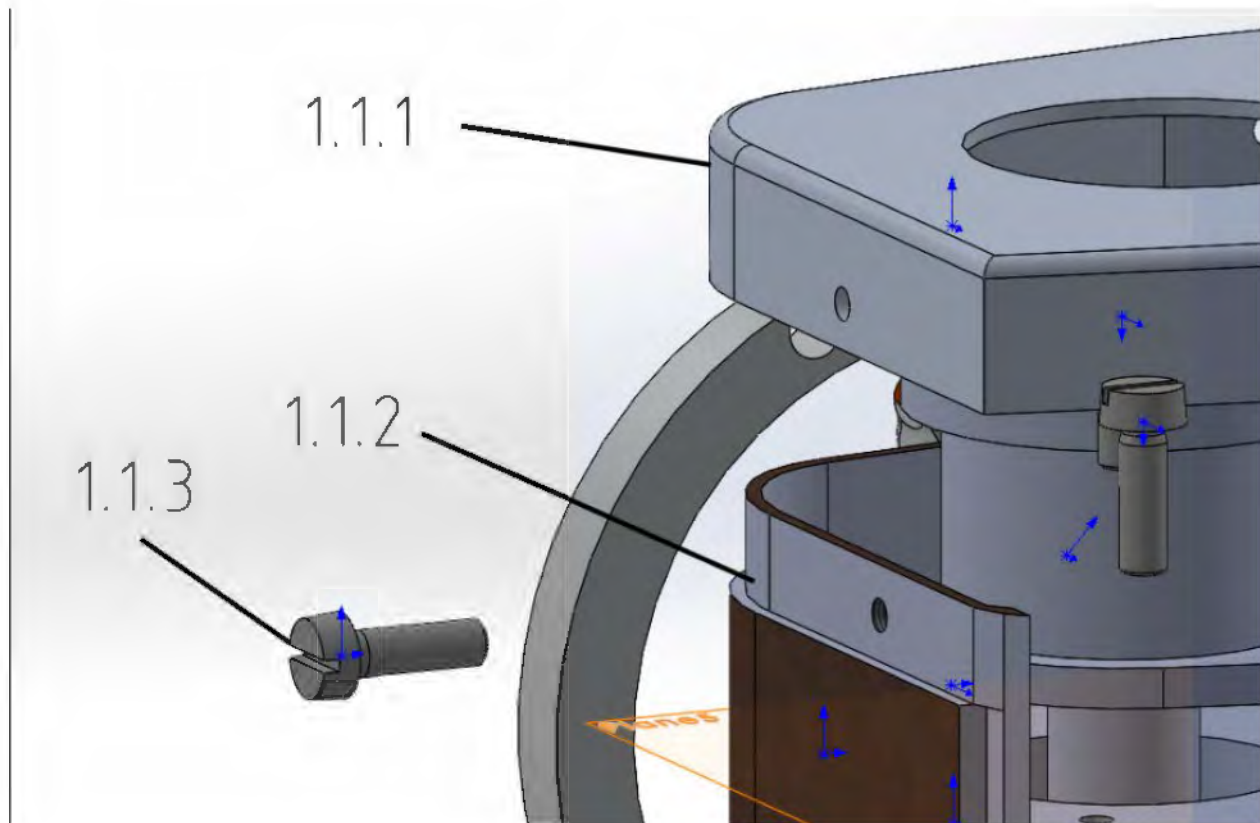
Demostración 3d de ensamblaje 1.1.1
